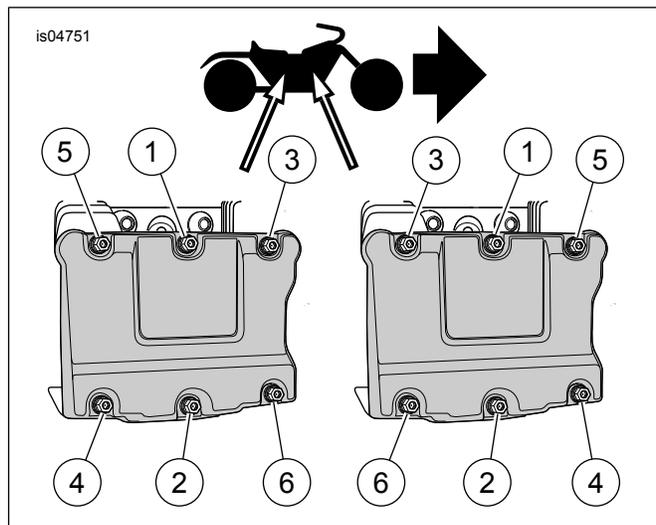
Sechs KIPPHEBELDECKELSCHRAUBEN in der abgebildeten Reihenfolge lockern.
